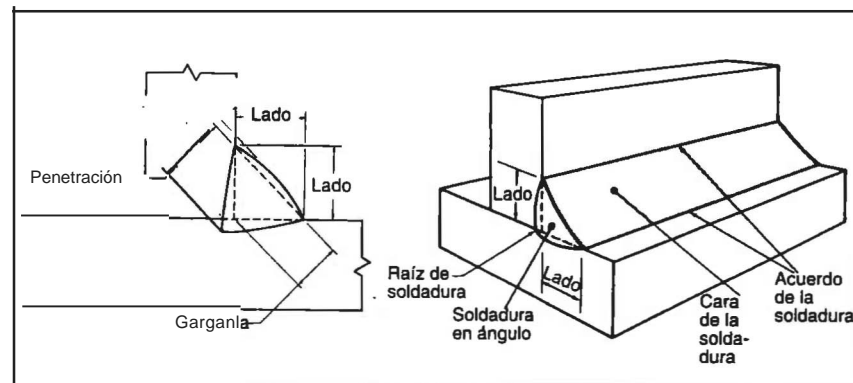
TERMINOLOGÍA DE LAS SOLDADURAS EN ÁNGULO
